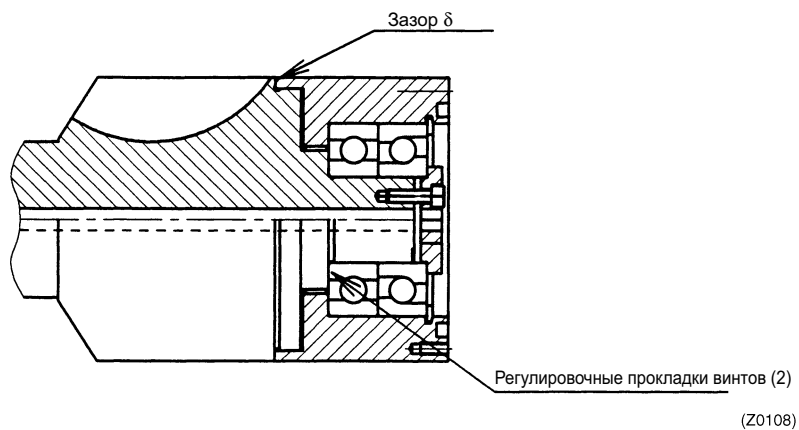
Регулировка зазора между винтовым ротором и главным держателем подшипников
